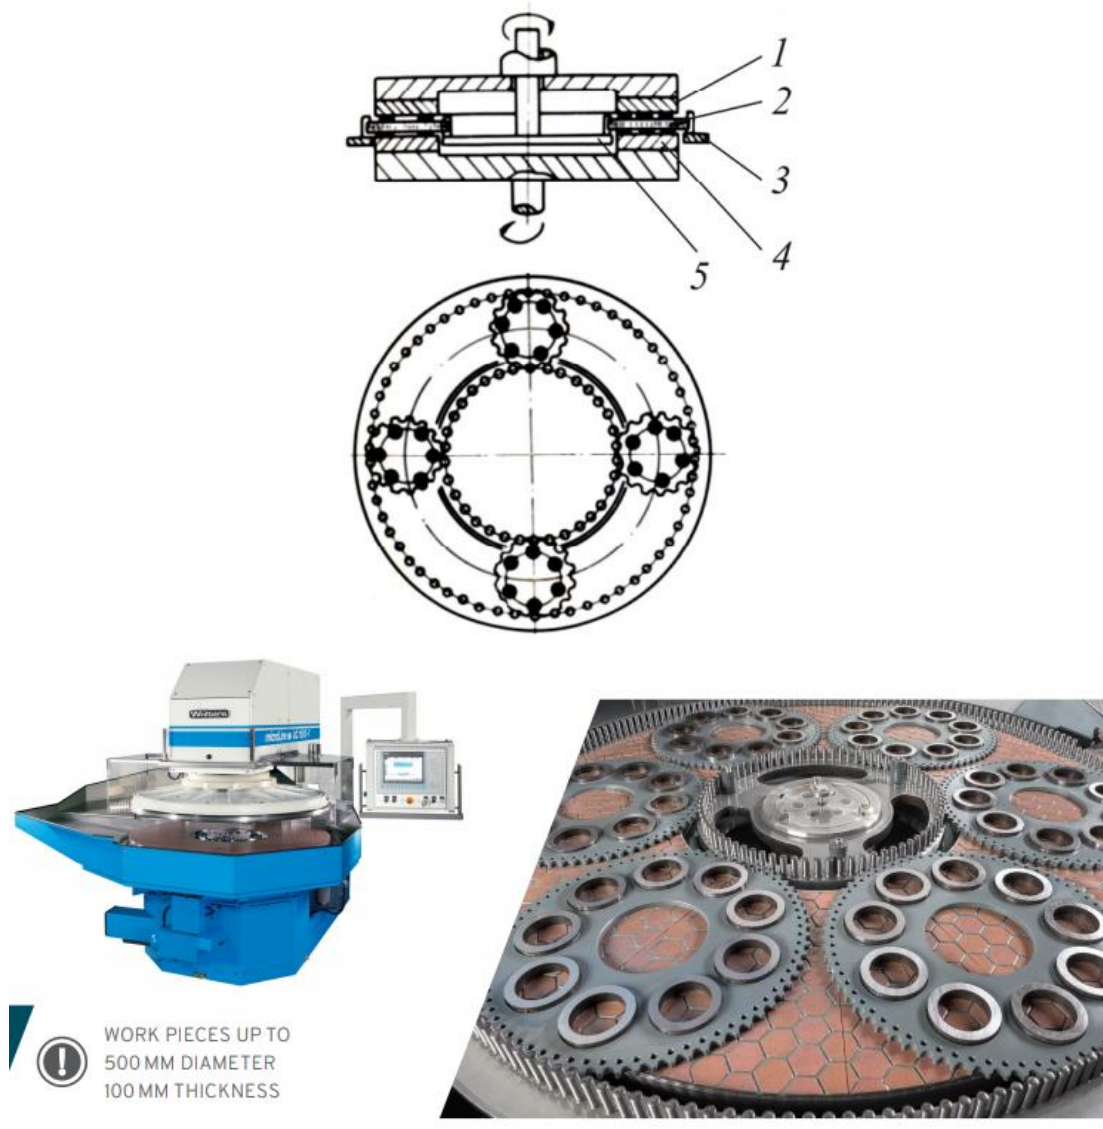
Схема верстата Peter Wolters з планетарними сепараторами
